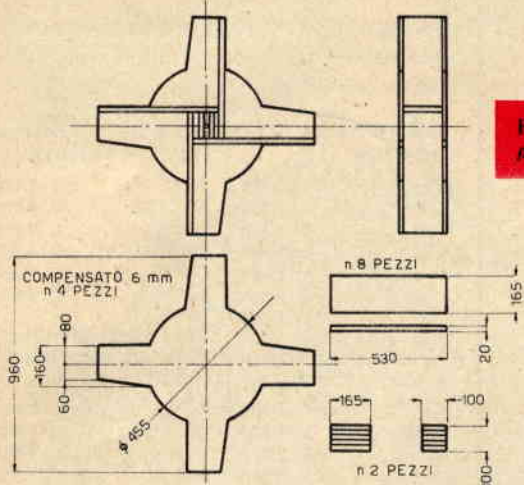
Dimensioni e profilo delle parti componenti le ruote a pale.
